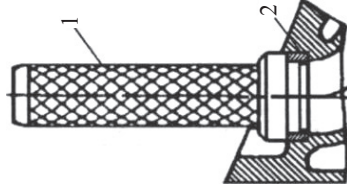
Запрессовка седла клапана с помощью оправки:
